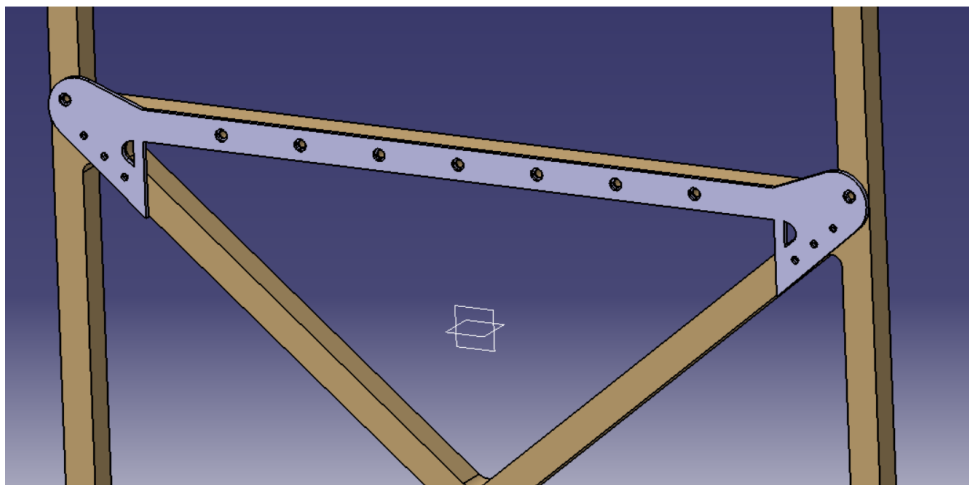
Refuerzo superior colocado sobre cuaderna 12
